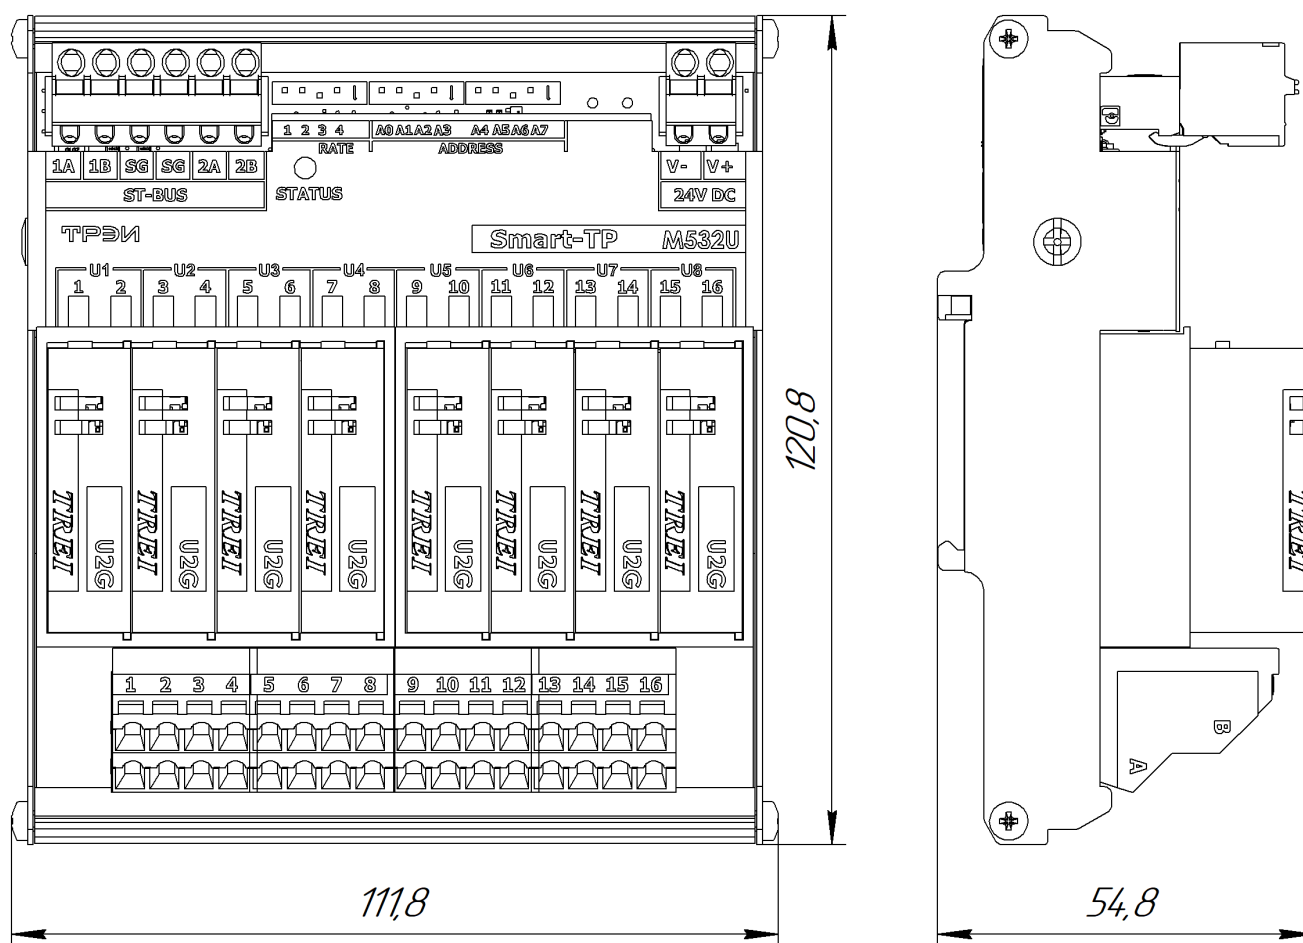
Чертеж общего вида M532U с указанием габаритных и присоединительных размеров
